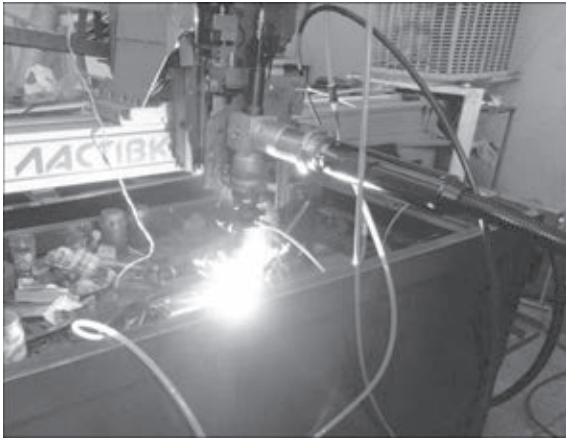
Процесс лазерной сварки двухсторонних стыковых соединений листового проката ВТ1-0 ДШП толщиной 12 мм, упрочненного азотом (0,098 мас. %) из газовой фазы в процессе ДШП
